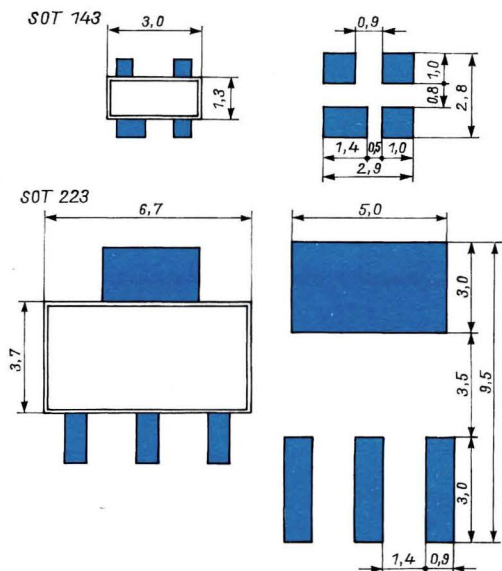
Bauformen und Abmessungen einiger SMD-Bauelemente
